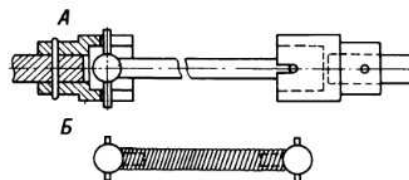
Соединение редукторов с двигателем: А — шарнирное, валиком; Б — шарнирное, гибким валиком.
